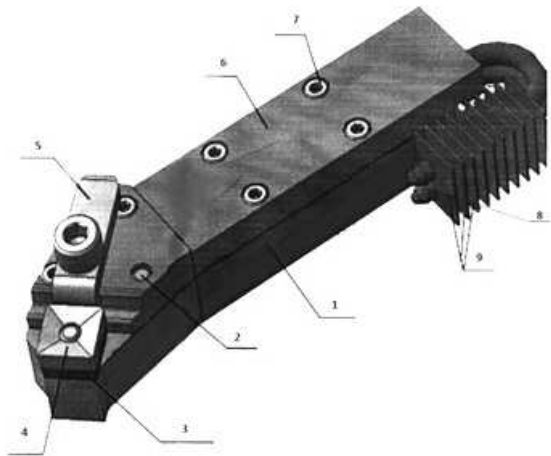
Резец с КСО в собранном виде: 1 - державка; 2 - опорный палец; 3 - опорная пластина; 4 - режущая пластина; 5 - прижим; 6 - крышка; 7 - соединительные винты; 8 - тепловые трубы; 9 - пластины радиатора
